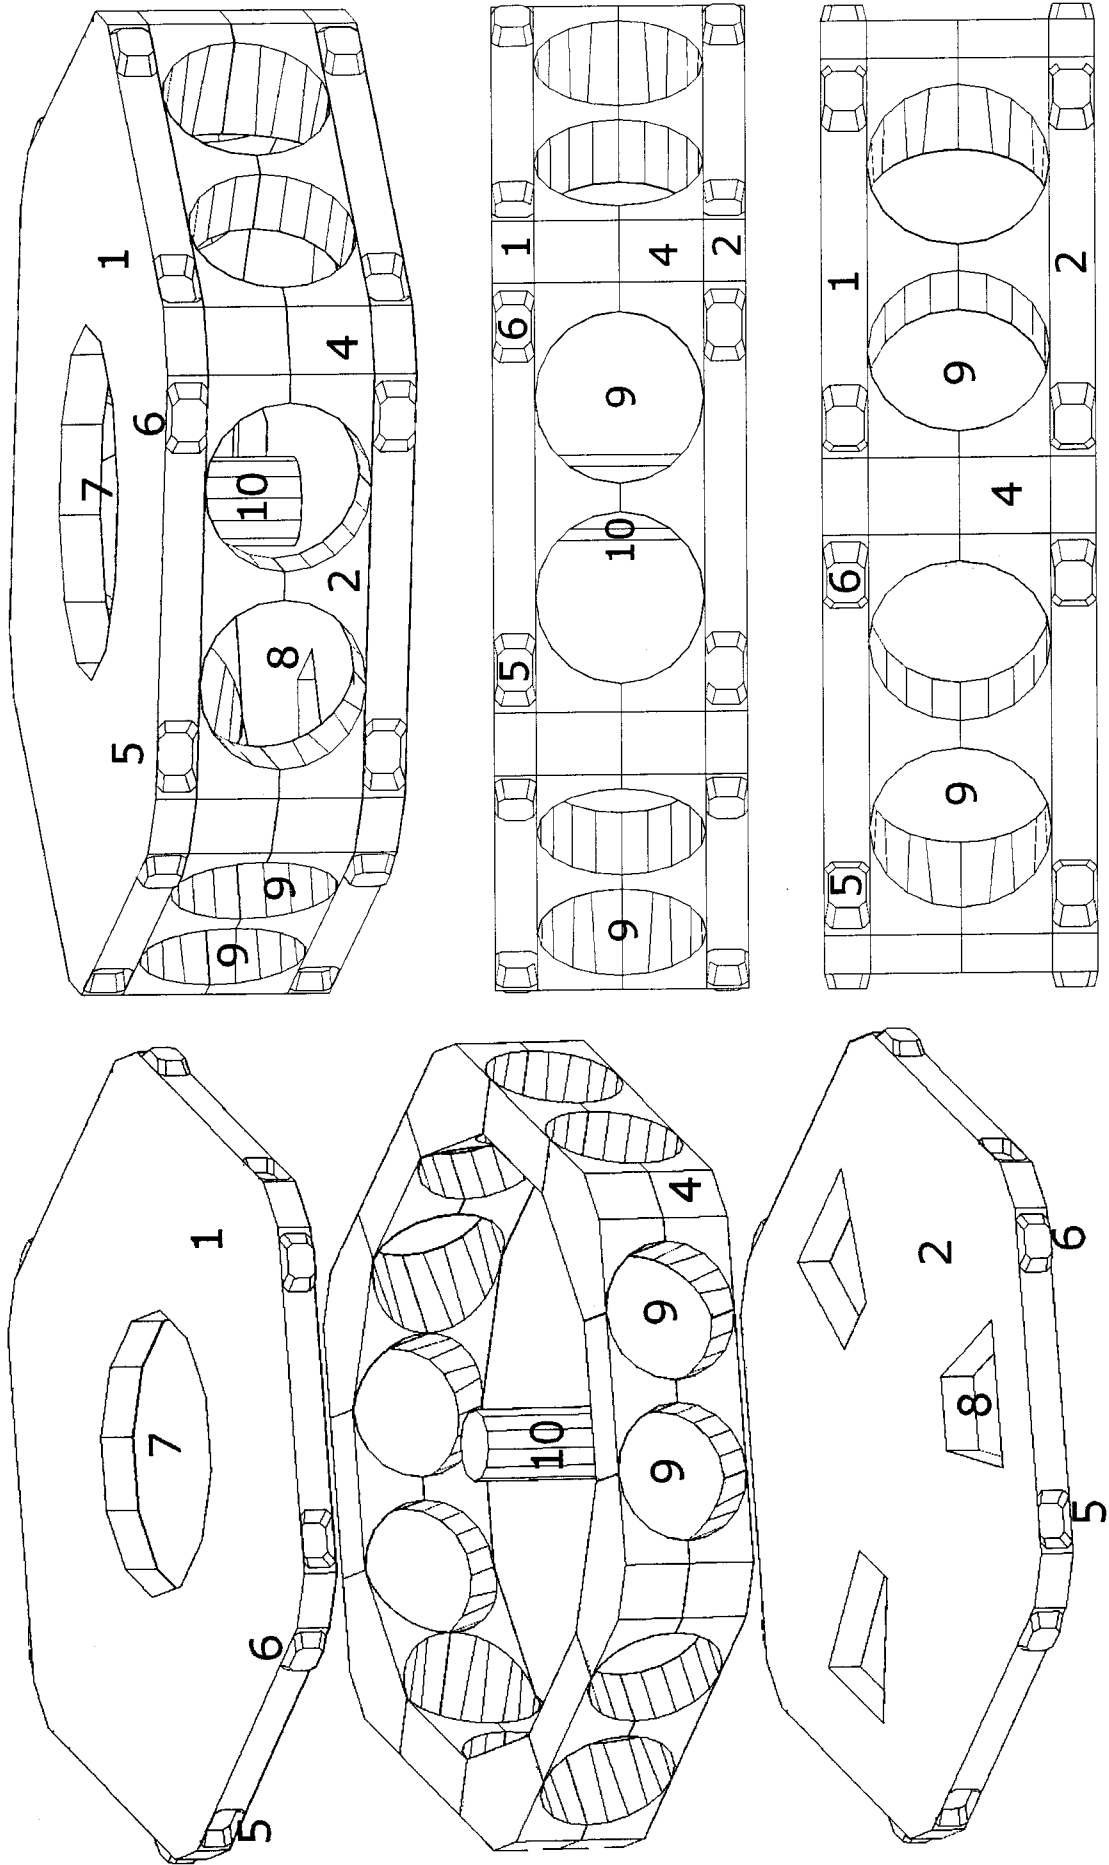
Estructura Resistente - Versión ANILLO ALIGERADO: Despiece y Vistas 3D , Perfil y Planta
